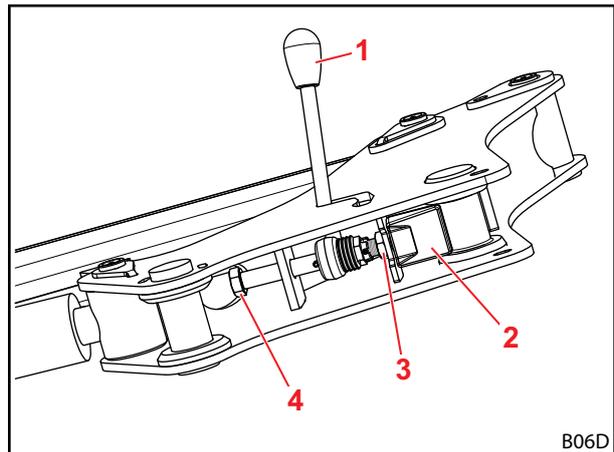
Vista del dispositivo di bloccaggio del caricatore frontale dal basso
